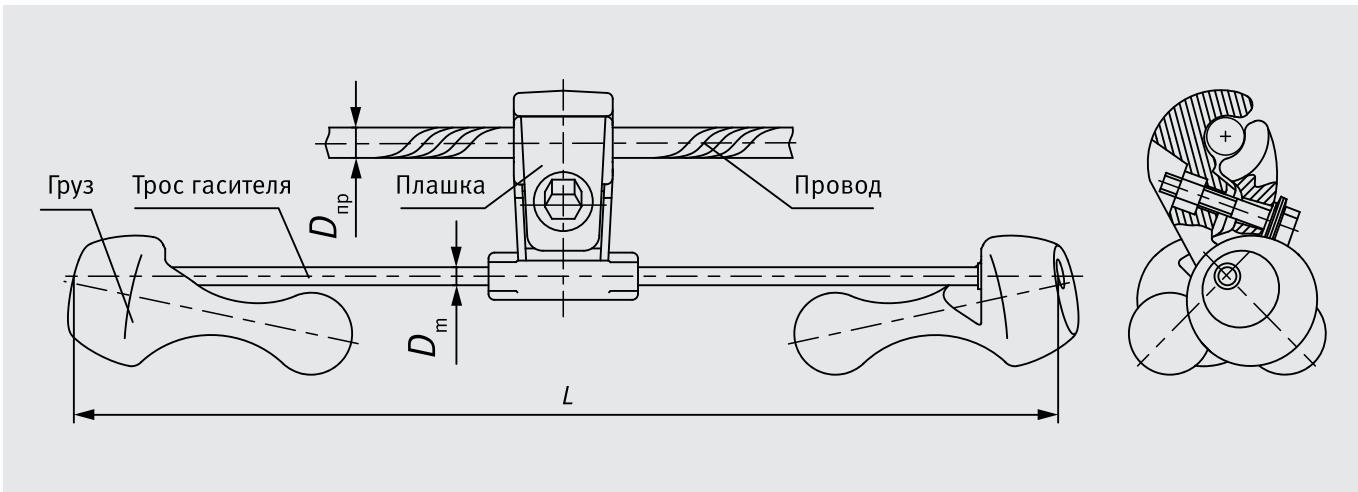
Гаситель вибрации марки ГВ-XXXX-02
